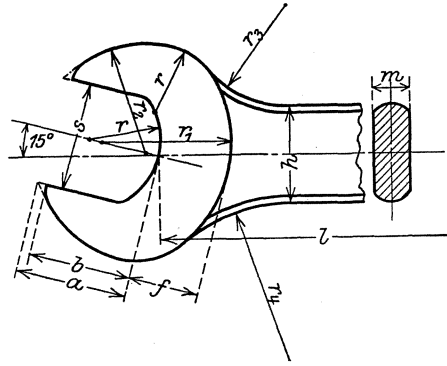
Schraubenschlüssel nach Dinorm 129 und 133.
